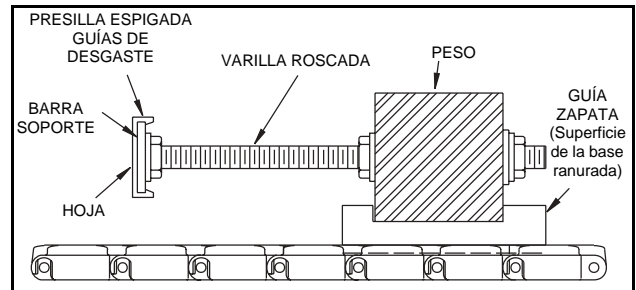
CONJUNTO DE LA BARRA EMPUJADORA
